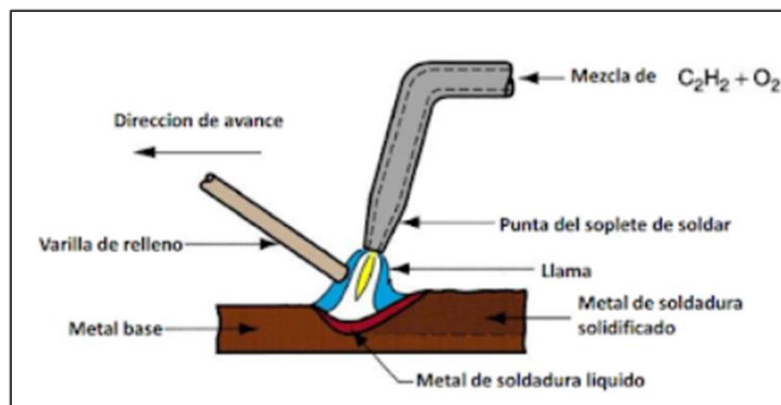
Proceso de soldadura oxiacetilénica OAW
